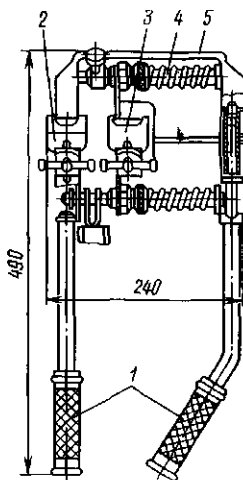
Клещи АТСР50-185 для термитной сварки проводов
